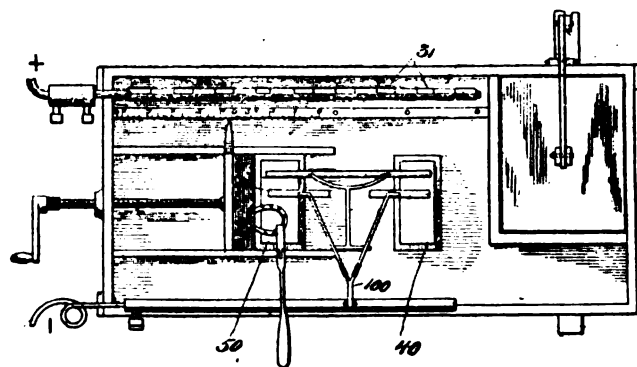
à 6. — Soudure électrique d'une bride
